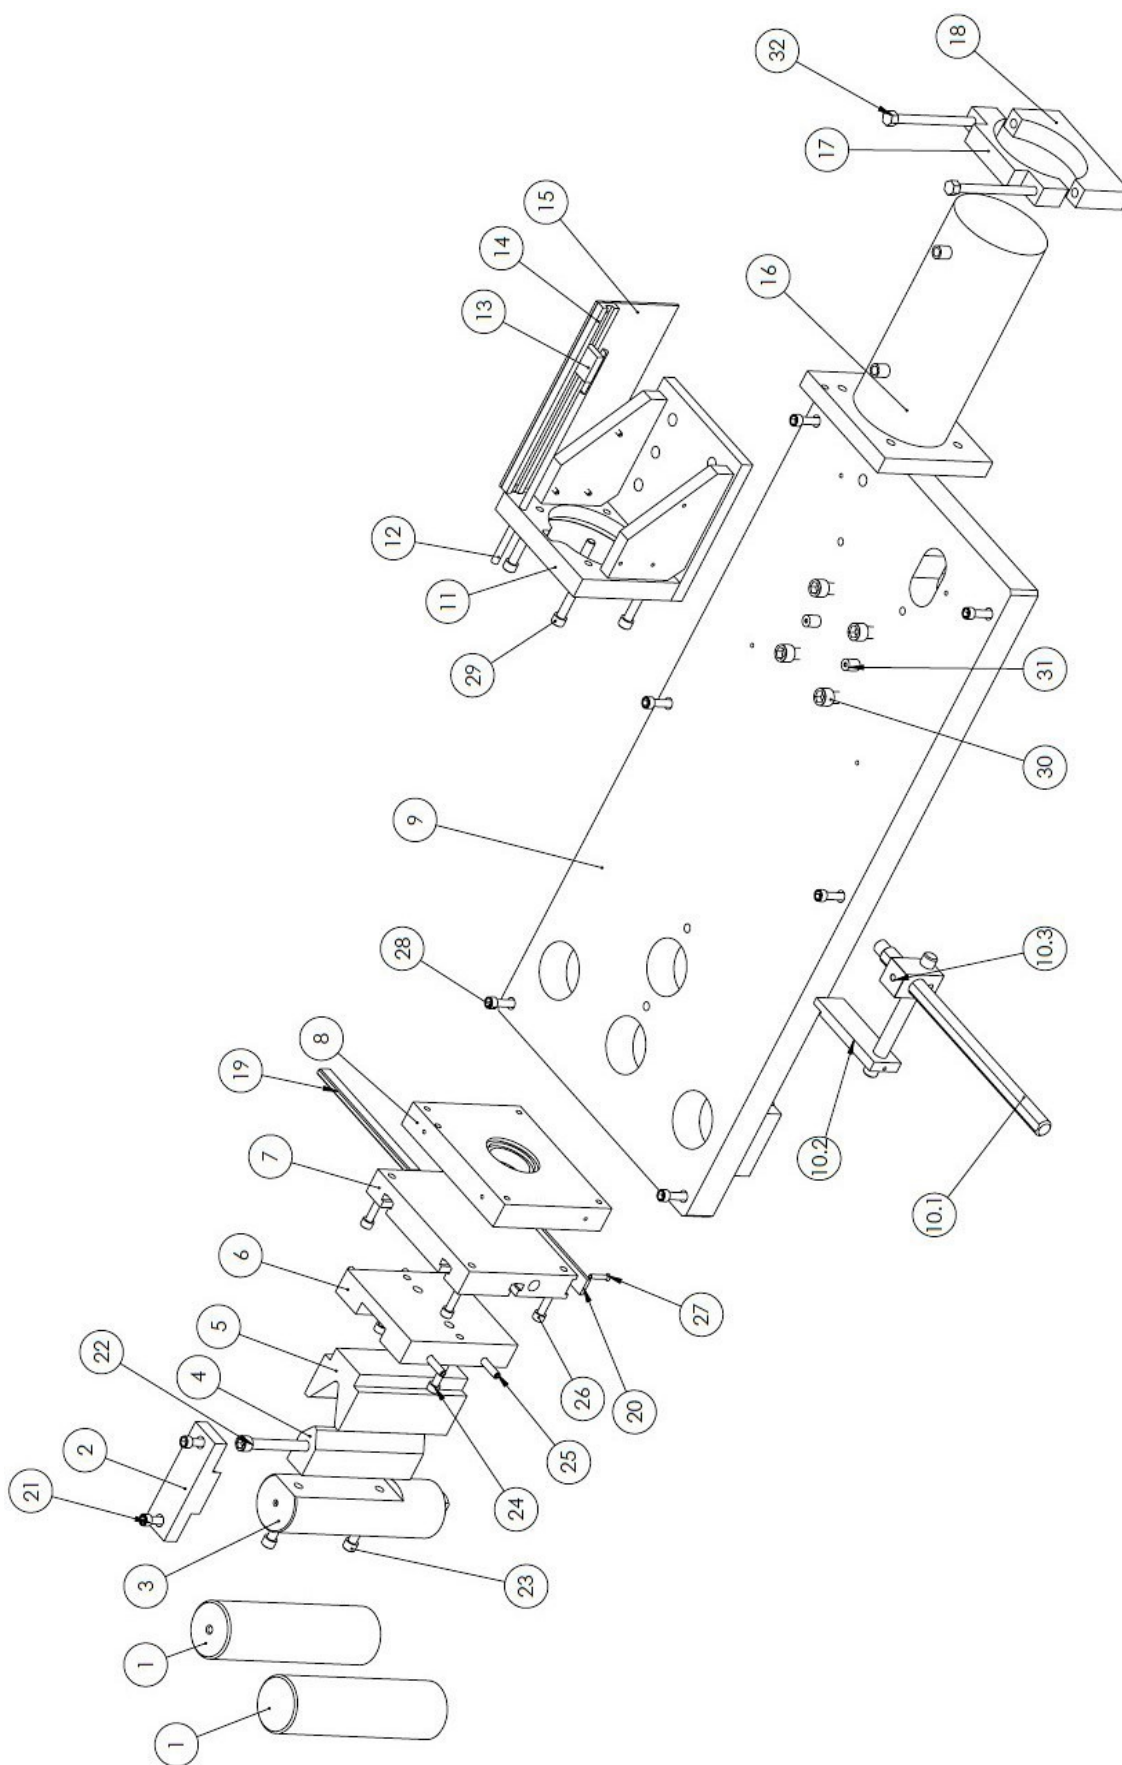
Schéma des pièces 2 Zone de travail HBP 20
